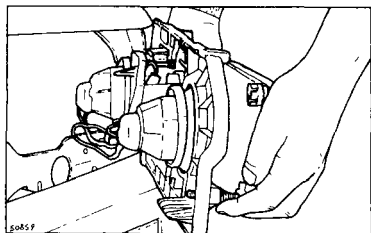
Извлеките блок фар из корпуса (Renault 11)
